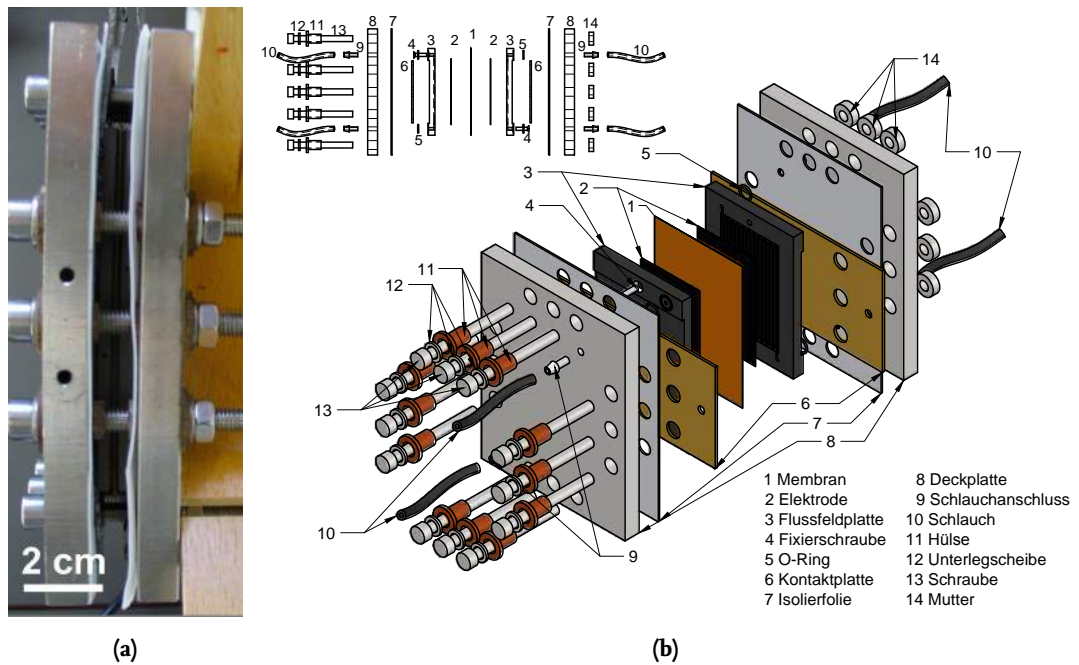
(a) Foto und (b) Explosionszeichnung von Zelle NC-1.
